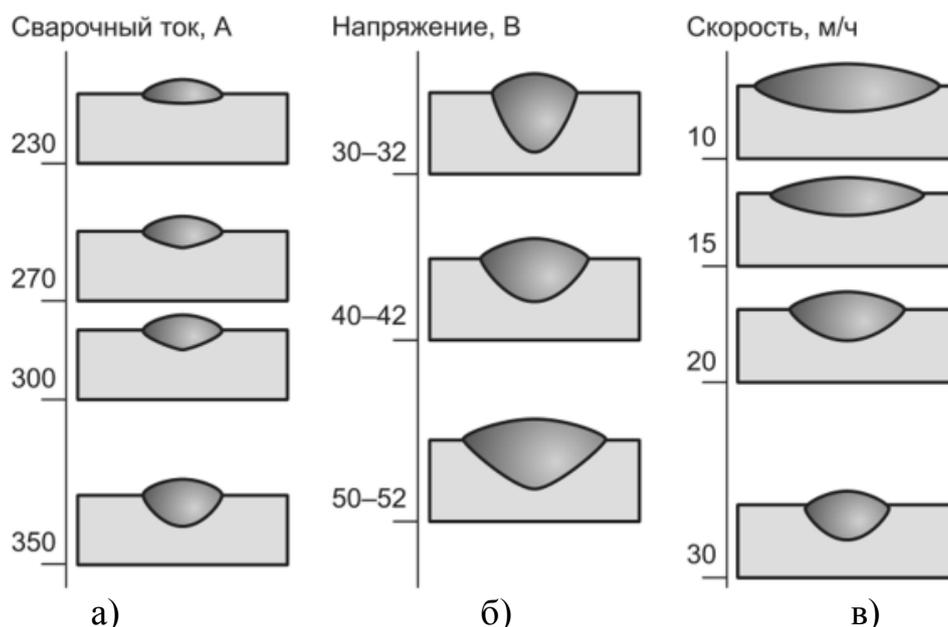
Влияние на форму и размеры шва сварочного тока (а), напряжения дуги (б), скорости сварки (в)
